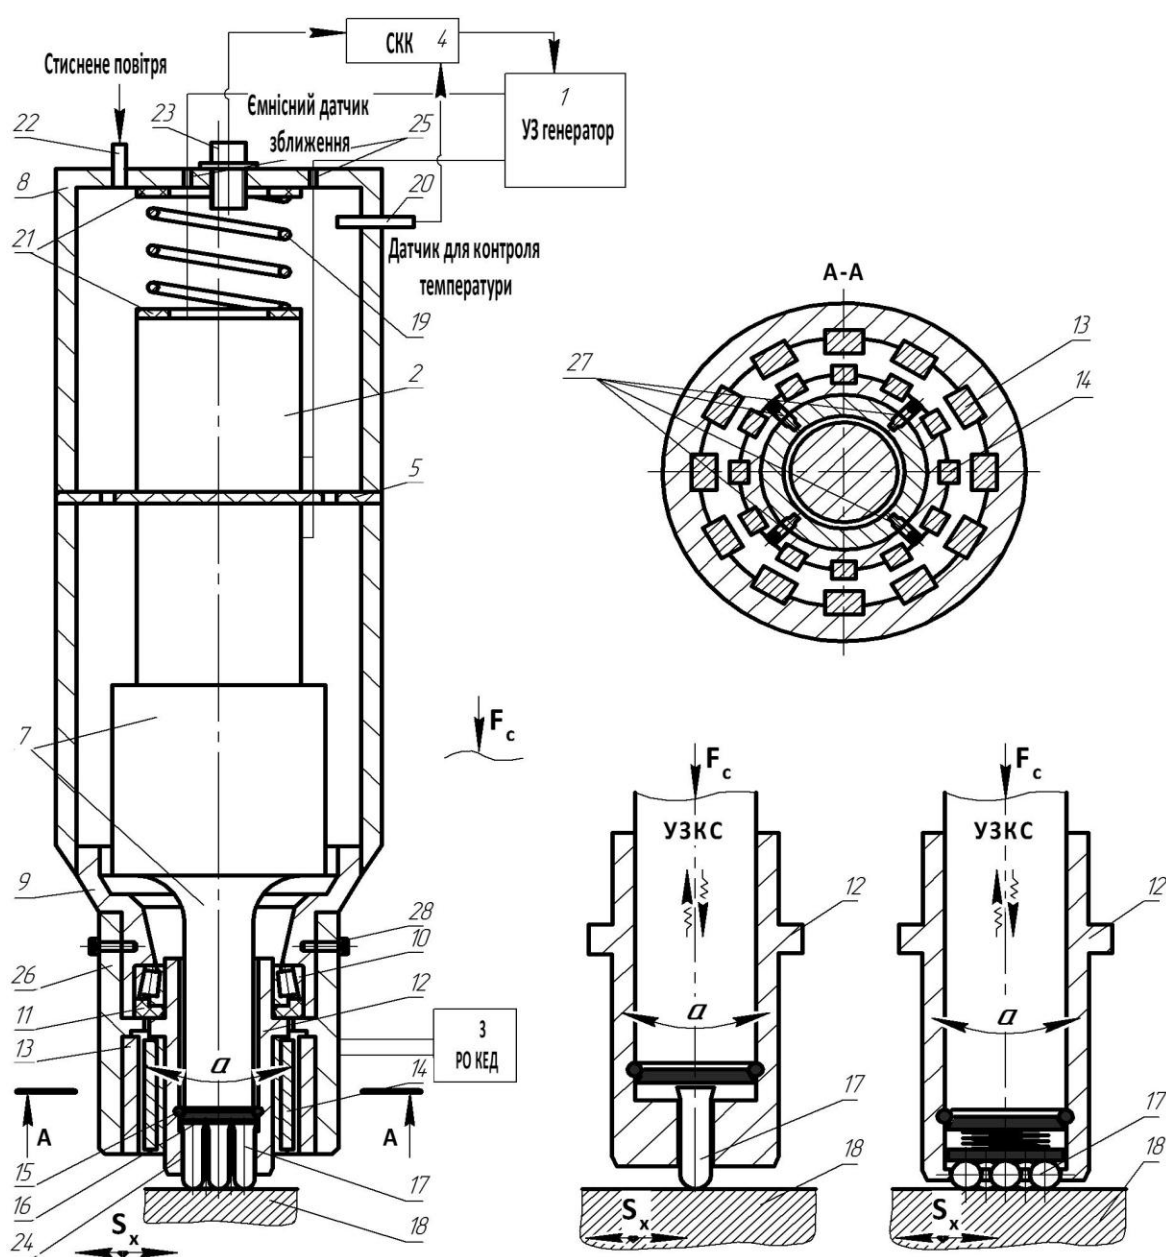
Конструкція установки для поверхневої УЗО
